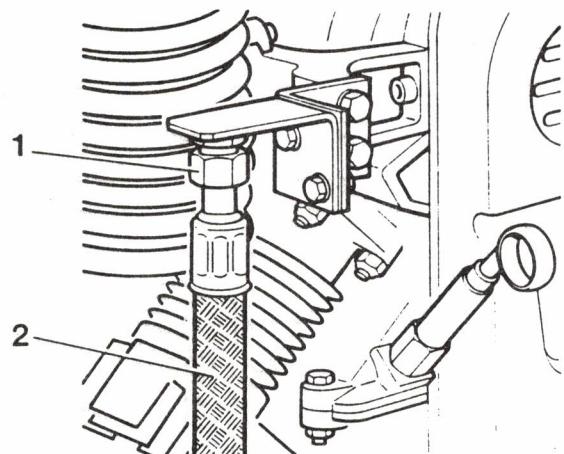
Ölablaßschlauch, Drucklufterzeuger (EliMot)
